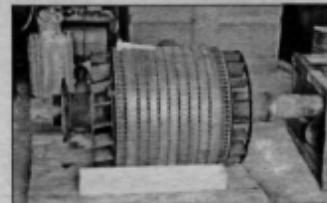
Ротор електродвигуна з відновленими посадочними поверхнями під підшипники. Відновлення здійснено шляхом газопорошкового напилення порошком П-12Н-01.
